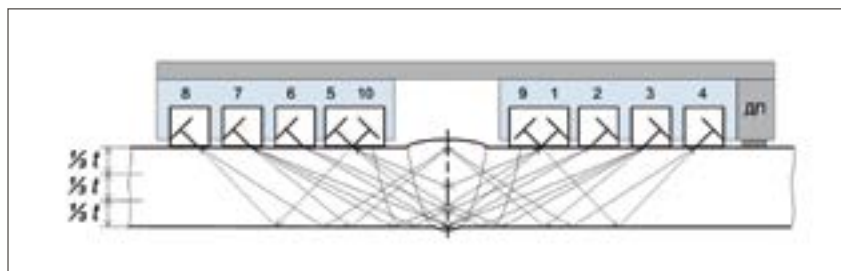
Потактовое прозвучивание сечения сварного шва:
